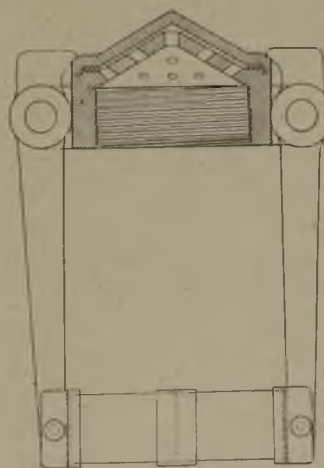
Nach oben gerichtete Feuerlöschvorrichtung.
